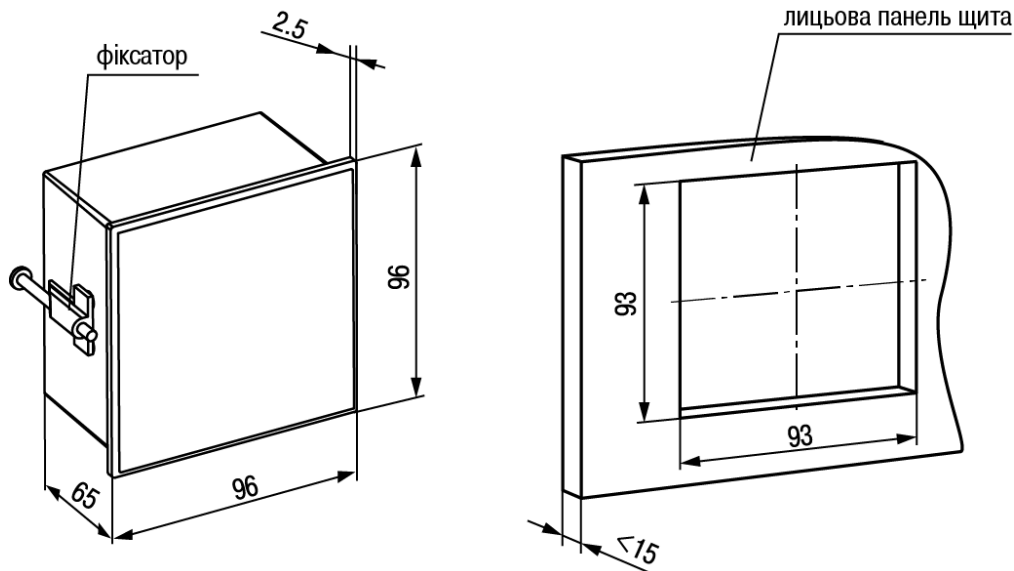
Габаритні розміри корпусу Щ1
